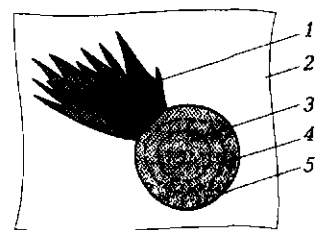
Внутренний выплеск металла при точечной контактной сварке:
